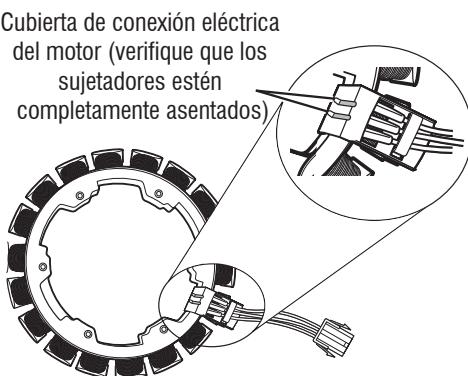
Extracción de la bobina del actuador y revisión de la conexión eléctrica del motor
